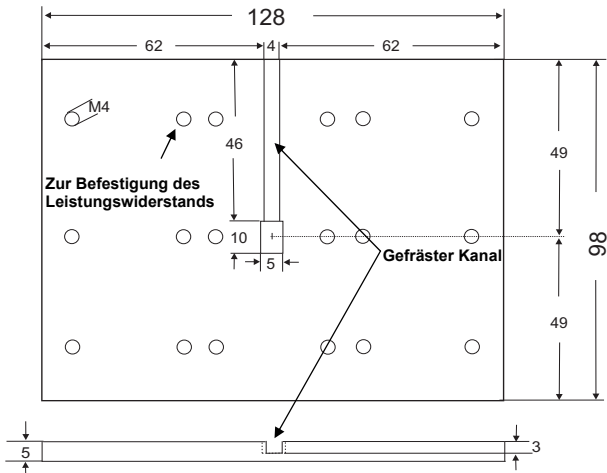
Die Kupferplatte mit gefrästem Kanal zur Befestigung der Wärmequelle
